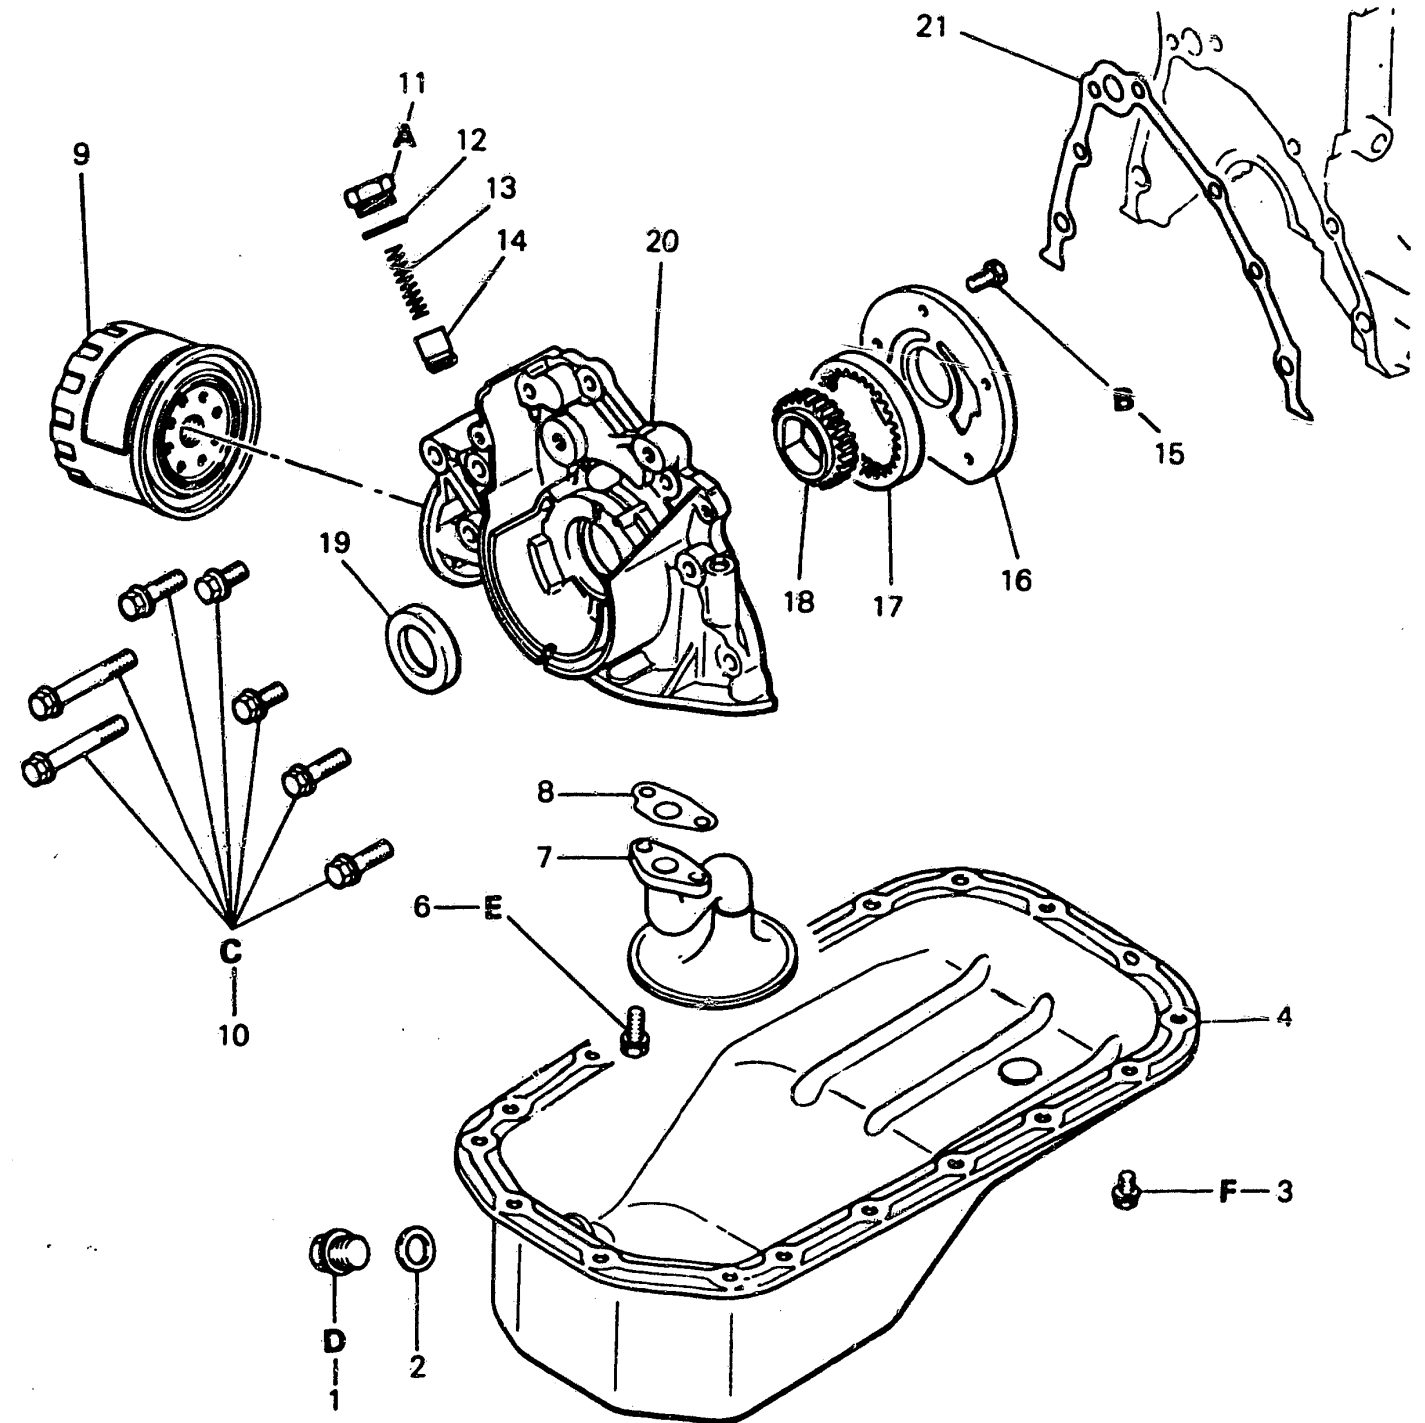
Einzelteile der Ölpumpe: 1 Ölablassschraube – 2 Dichtung der Ölablassschraube – 3 Schraube (18) – 4 Ölwanne – 6 Schraube (2) – 7 Ölfiltersieb – 8 Ölfiltersiebichtung – 9 Ölfilter – 10 Flanschschraube (7) – 11 Verschlusschraube – 12 Dichtung – 13 Überdruckventilfeder – 14 Überdruckventil – 15 Schraube (5) – 16 Ölpumpendeckel – 17 Äusseres Ölpumpen-Zahnrad – 18 Inneres Ölpumpen-Zahnrad – 19 Wellendichtung – 20 Steuergehäuse – 21 Dichtung. Die Zahlen entsprechen der Demontage-Reihenfolge.
